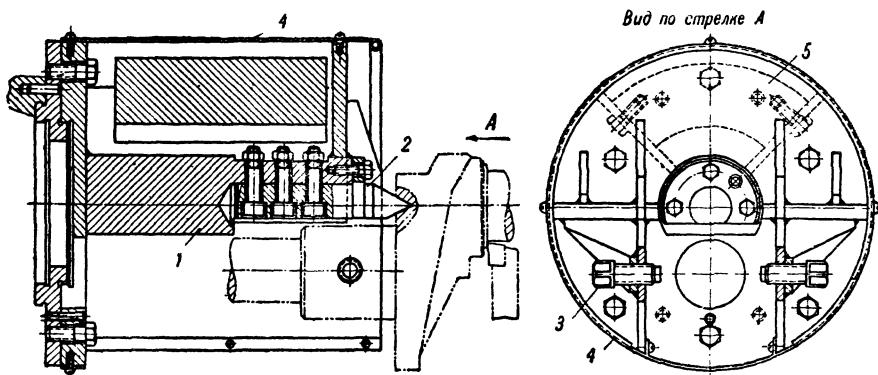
Приспособление для обработки коленчатого вала рис. 200.
